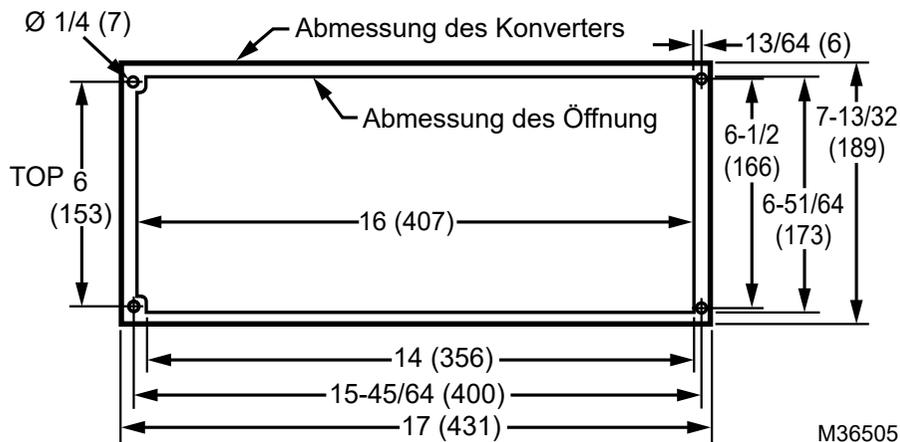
Abmessungen Ausschnitt für Flanschmontage für MI5 [Unit: Inches (mm)]
